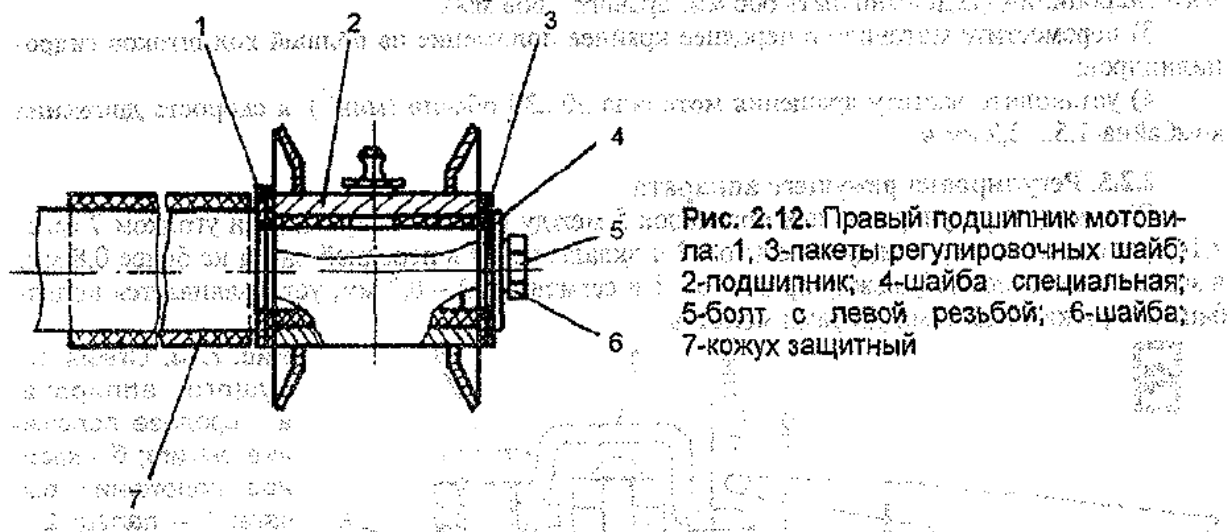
Правый подшипник мотовила; 1, 3-пакеты регулировочных шайб; 2-подшипник; 4-шайба специальная; 5-болт с левой резьбой; 6-шайба; 7-кожух защитный
